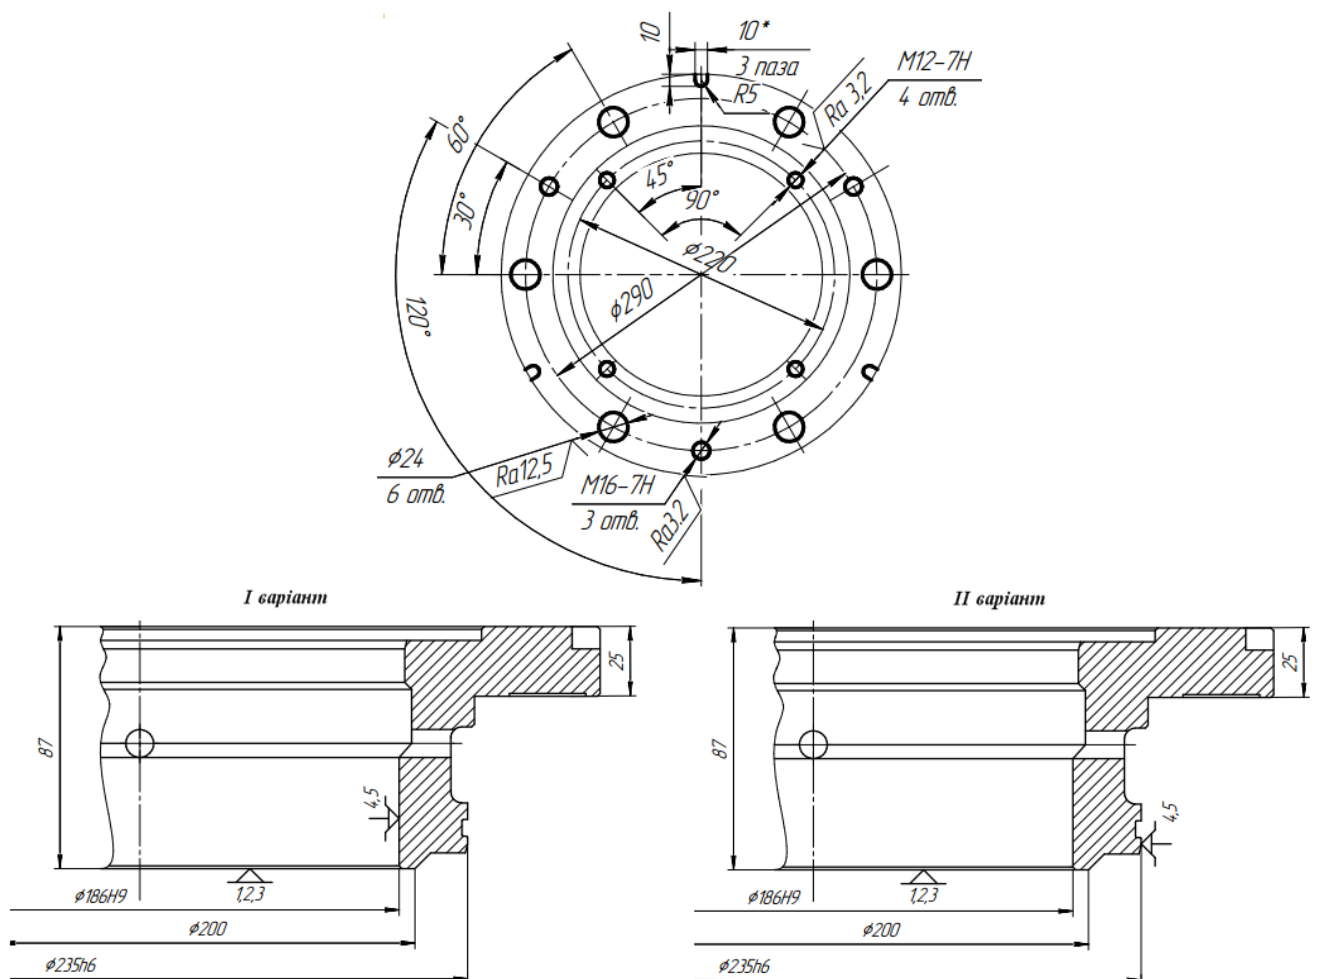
Можливі варіанти базування на операції «050 Фрезерна з ЧПК»
